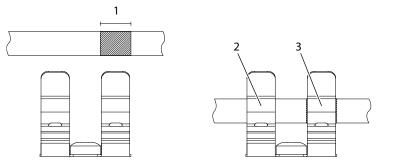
Decapagem do cabo e uso das placas de instalação condutoras
